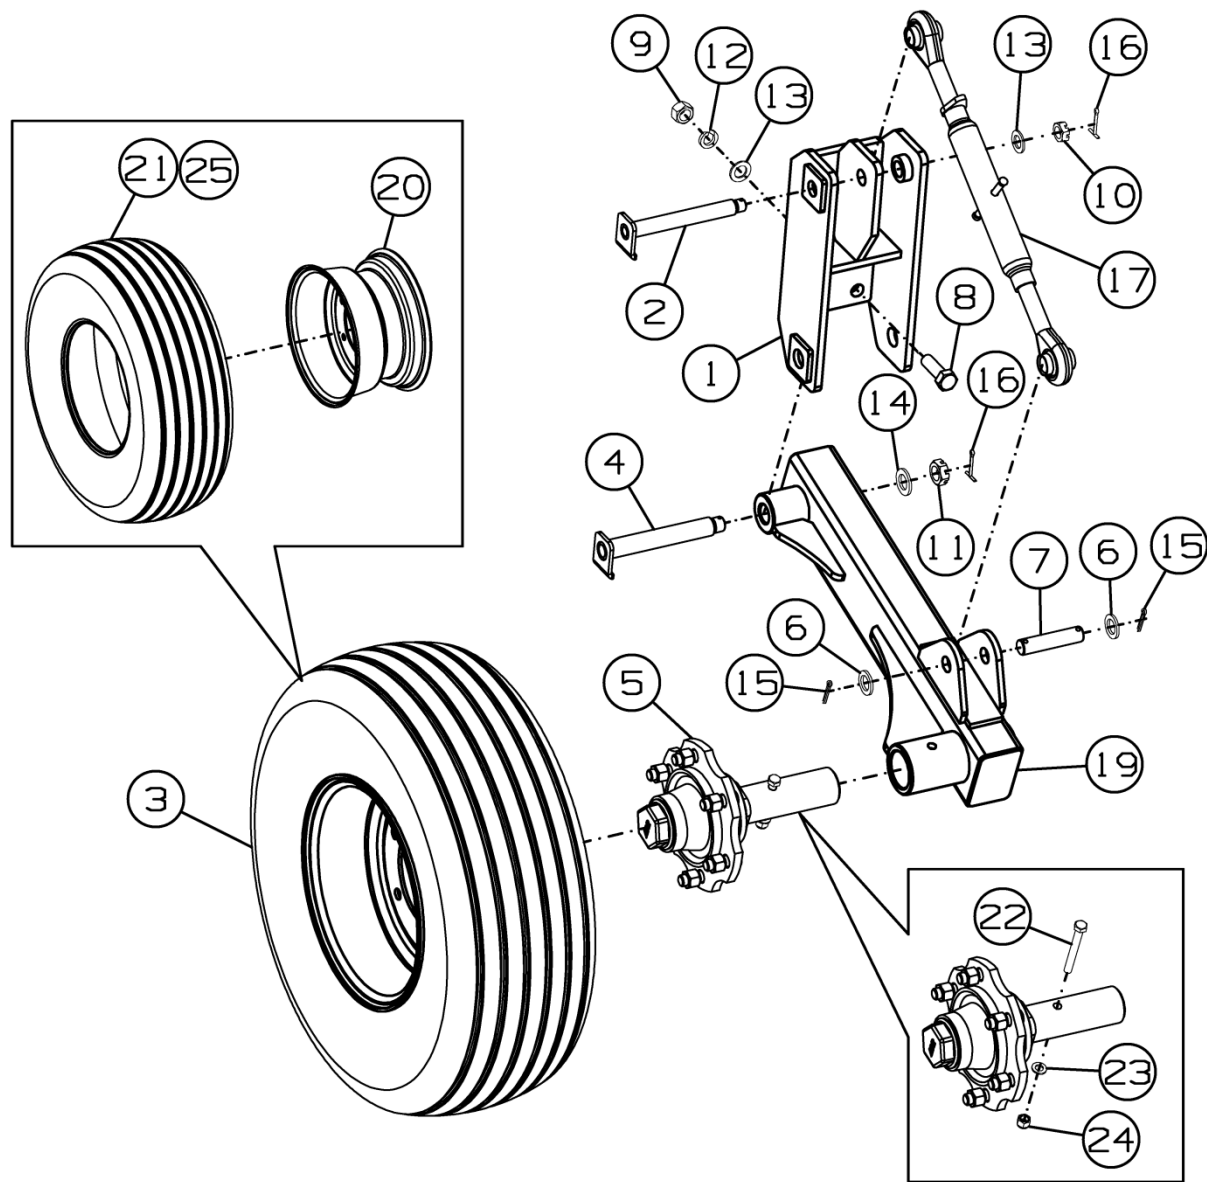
Колесо опорное СГ-122.06.000-01
